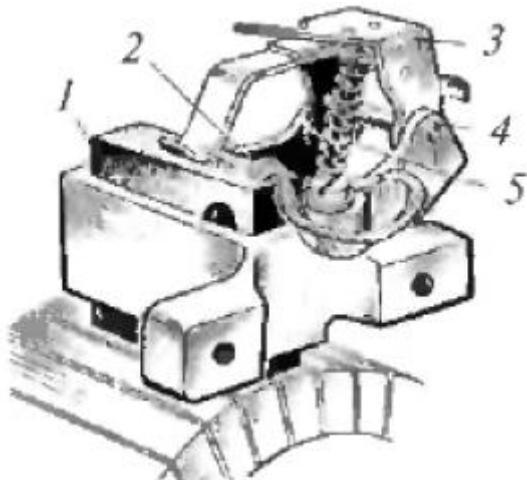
Пример конструкции щеточного узла: 1 — щетка; 2 — гибкий шунт; 3 — нажимной палец; 4 — корпус щеткодержателя; 5 — пружина.
